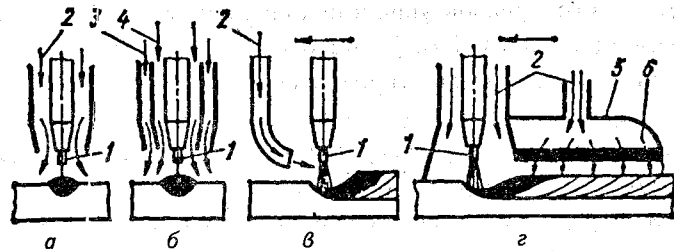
Подача защитных газов в зону сварки: а — центральная одним concentрическим потоком; б — центральная двумя concentрическими потоками; в — боковая; г — в подвижную камеру (насадку); 1 — электрод; 2 — защитный газ; 3, 4 — наружный и внутренний потоки защитных газов; 5 — насадка; 6 — распределительная сетка
